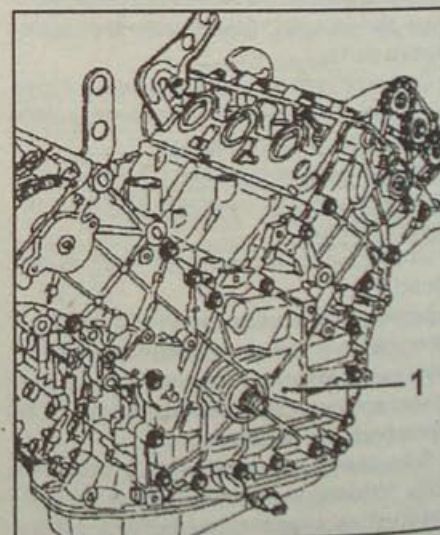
Расположение крышки (1) привода газораспределительного механизма
